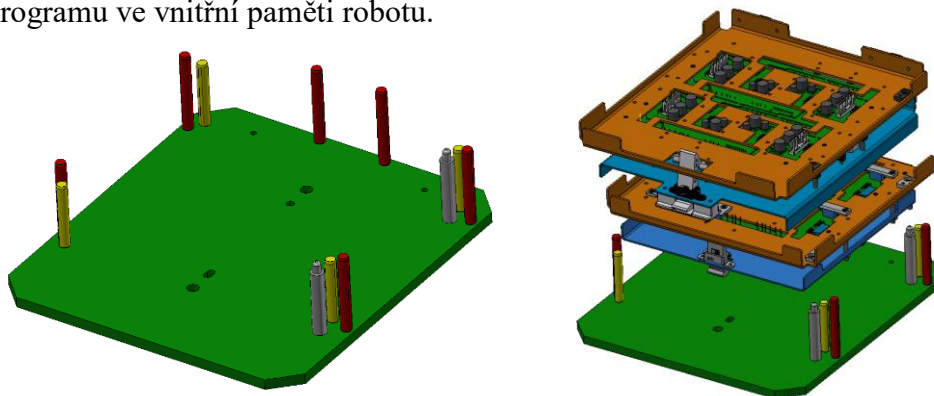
Fixátory termistorů, vlevo původní konstrukce a vpravo je změněná
